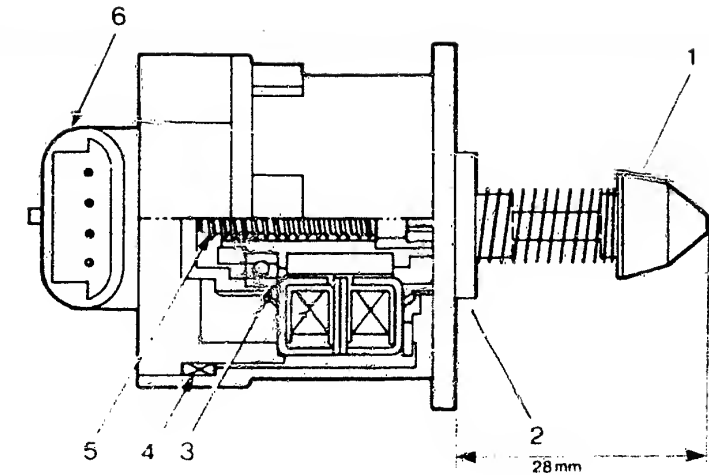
Der Leerlauffüllungs-Schrittmotor teilweise geschnitten: 1 Ventilkegel - 2 vorderes Lager - 3 hinteres Lager - 4 O-Ring - 5 Gewindespindel - 6 Anschlussstecker mit den Klemmen CADB.
